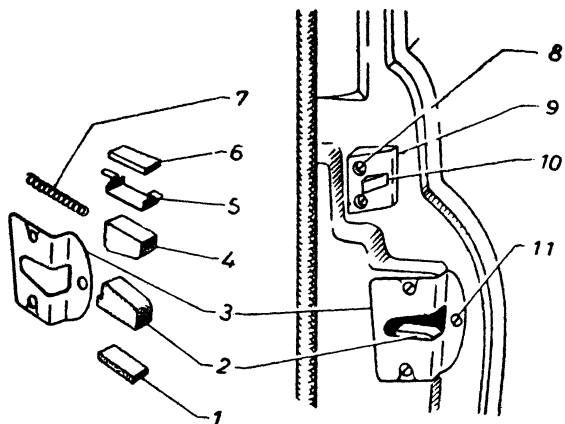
Вид на гнездо шипа и защелку замка двери (слева детали гнезда шипа в разобранном виде).
